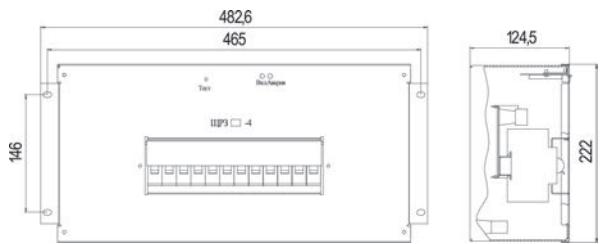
Габаритный чертеж ЩРЗ 24-4,
